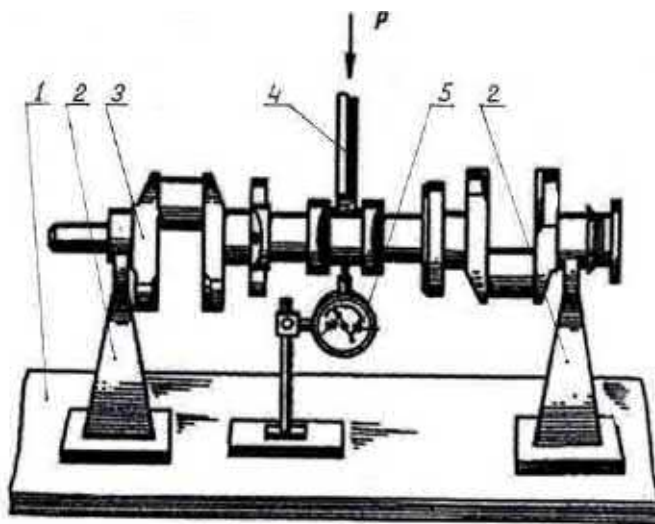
Классическая схема выпрямления коленчатого вала:
